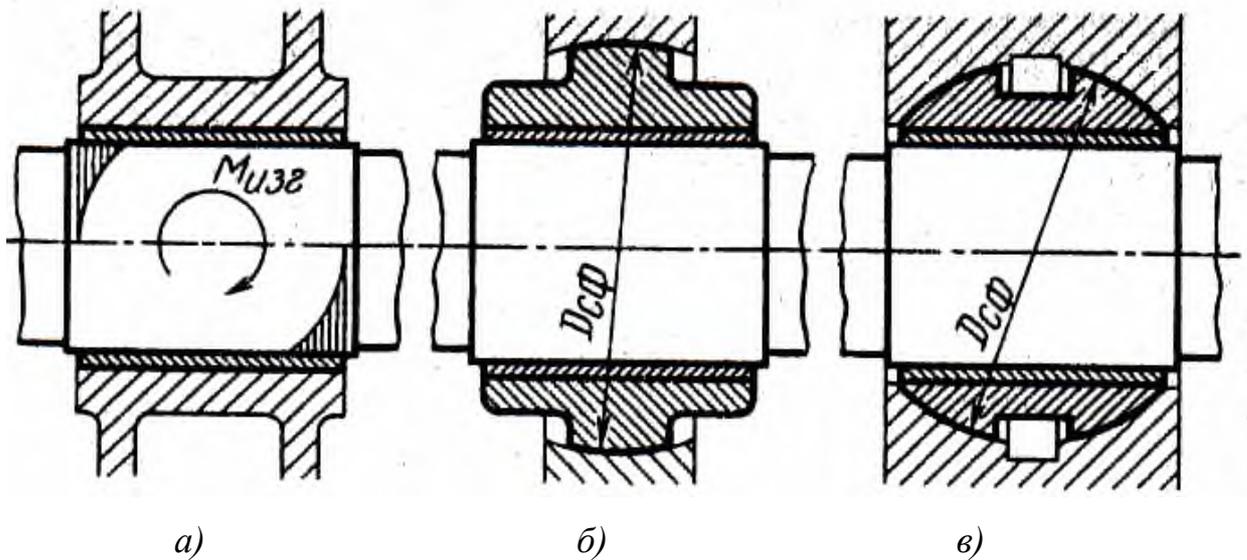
Обеспечение самоустанавливаемости подшипника скольжения
